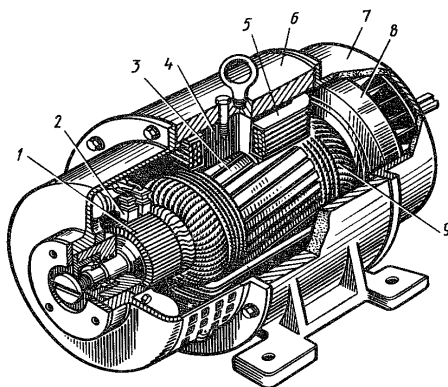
Устройство машины постоянного тока: 1 – коллектор; 2 – щетки; 3 – сердечник якоря; 4 – главный полюс; 5 – подушки обмотки возбуждения; 6 – корпус (станины); 7 – подшипниковый щит; 8 – вентилятор; 9 – обмотка якоря
